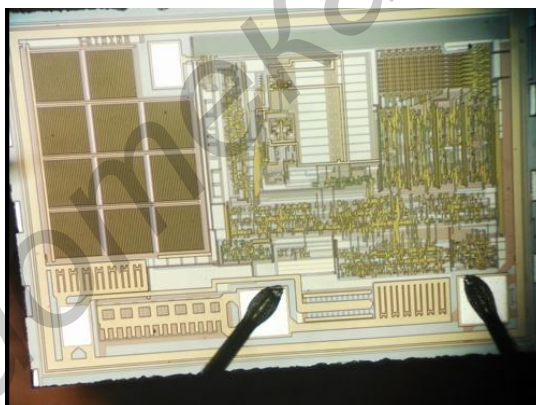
Внешний вид сварных соединений модулей на установке ЭМ-4371
